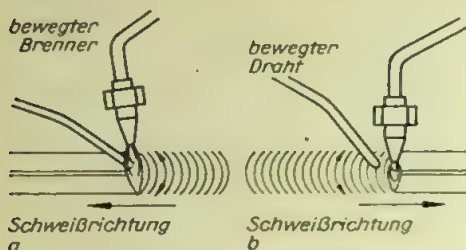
Gasschmelzschweißen: a Nach-links-Schweißen, b Nach-rechts-Schweißen
